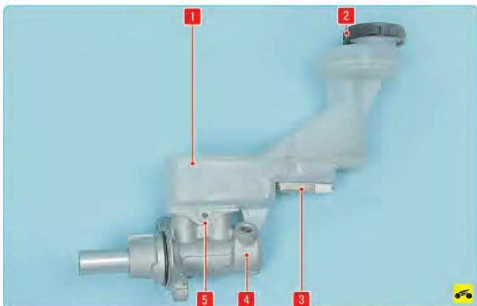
Главный тормозной цилиндр: 1 – бачок главного тормозного цилиндра; 2 – пробка бачка главного тормозного цилиндра; 3 – датчик уровня тормозной жидкости; 4 – главный тормозной цилиндр; 5 – фиксатор бачка
